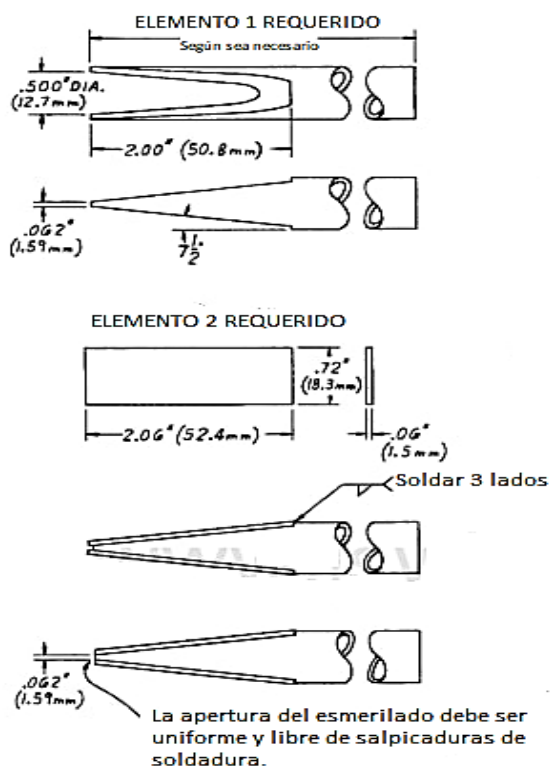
Diseño de la boquilla de acuerdo a la norma ASTM G65
